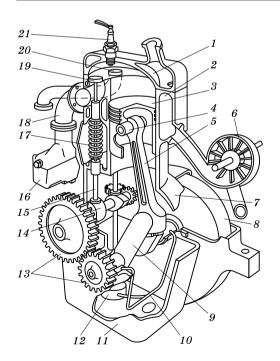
Устройство одноцилиндрового карбюраторного двигателя:
